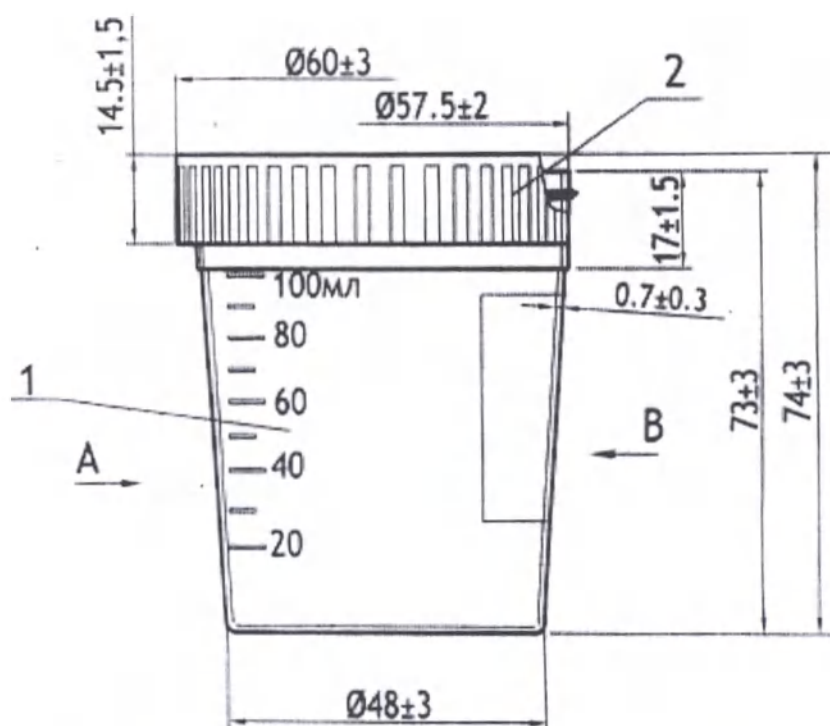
Контейнер для биопроб 60мл полимерный
